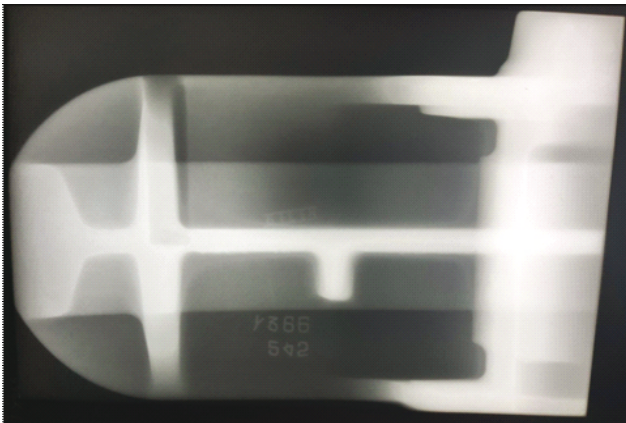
Obraz radiogramu obudowy wirnika odlew żeliwny.
